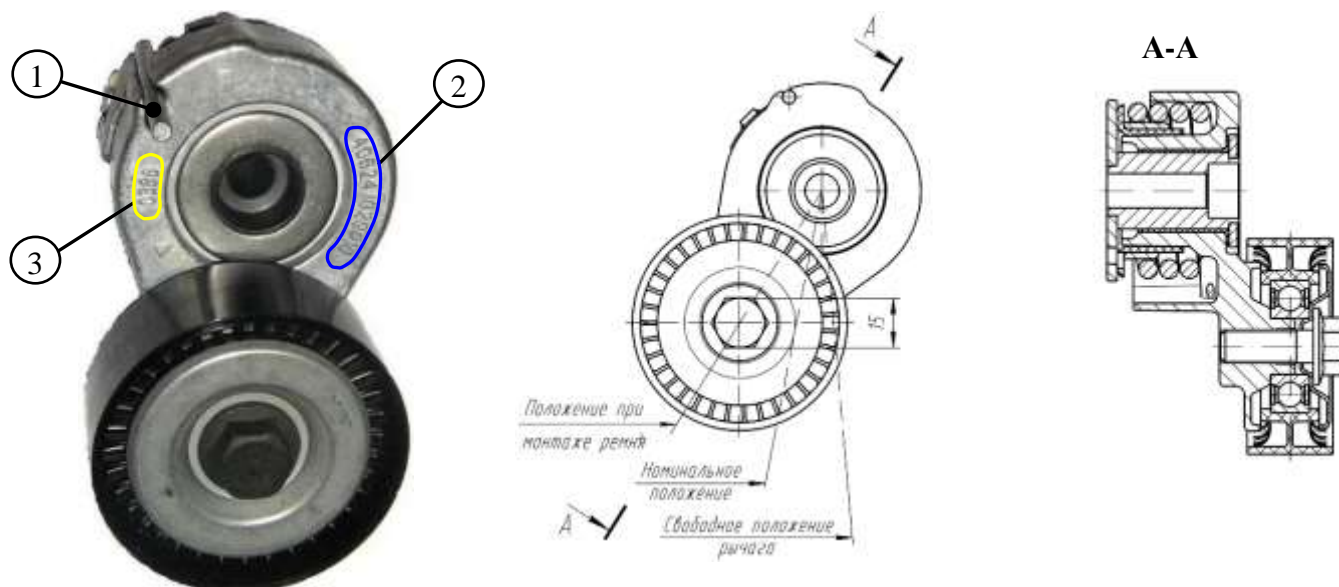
Внешний вид механизма автоматического натяжения ремня:
